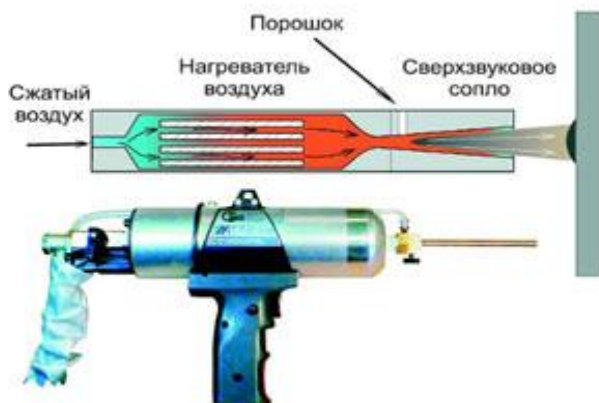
Схема сверхзвукового аппарата для напыления металлических покрытий
